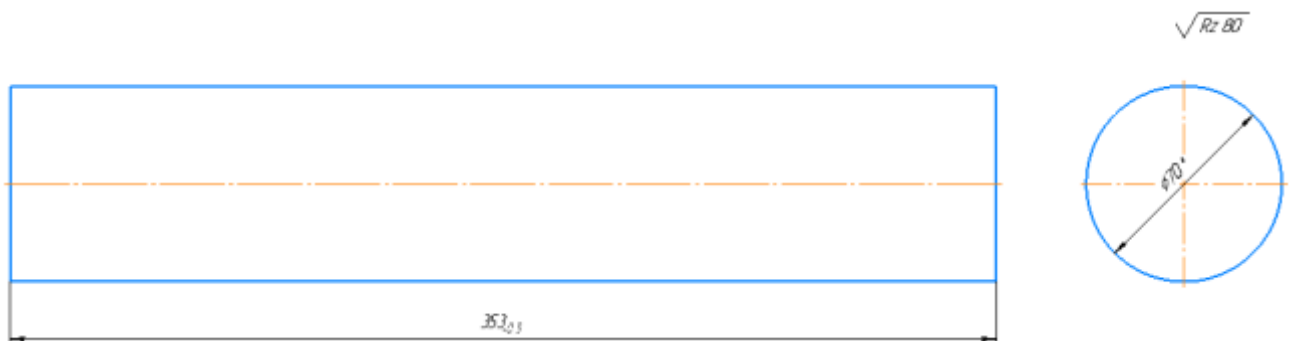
Эскиз заготовки из горячекатаного проката
